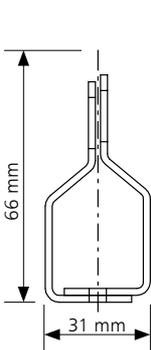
Ballastgewicht der feststehenden Rauchschürze Typ S
